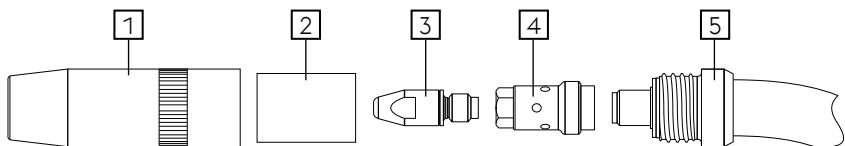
MT W ausrüsten / Setting up MT W / Équipement des torches MT W / Equipamiento de la MT W
